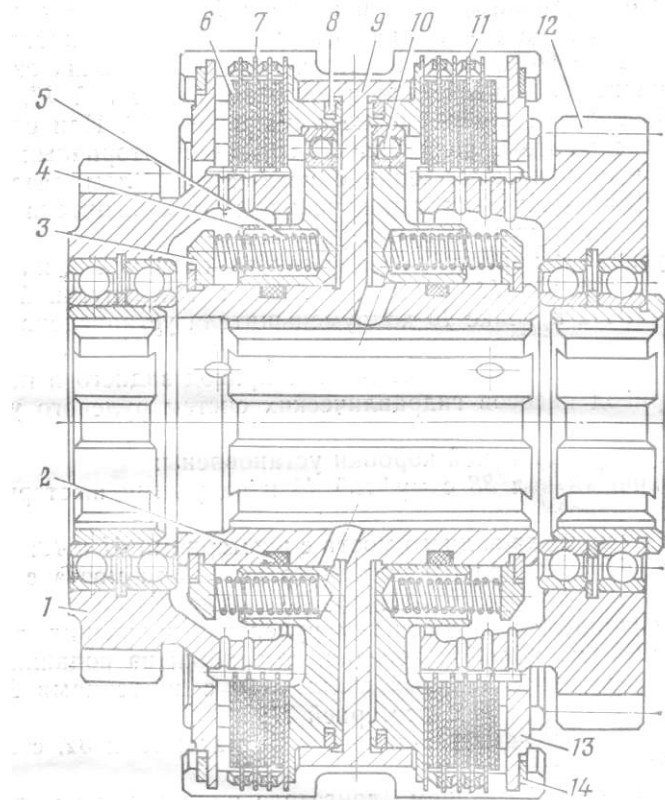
Гідропідтискна муфта: 1 і 12 - шестерні; 2 - кільце ущільнювача; 3 - упорна шайба; 4 - поршень; 5 - пружина; 6 - провідний диск; 7 і 11 - ведені диски; 8 - кільце поршня; 9 - барабан; 10 - зливний клапан; 13 - упорний диск; 14 - стопорне кільце.
